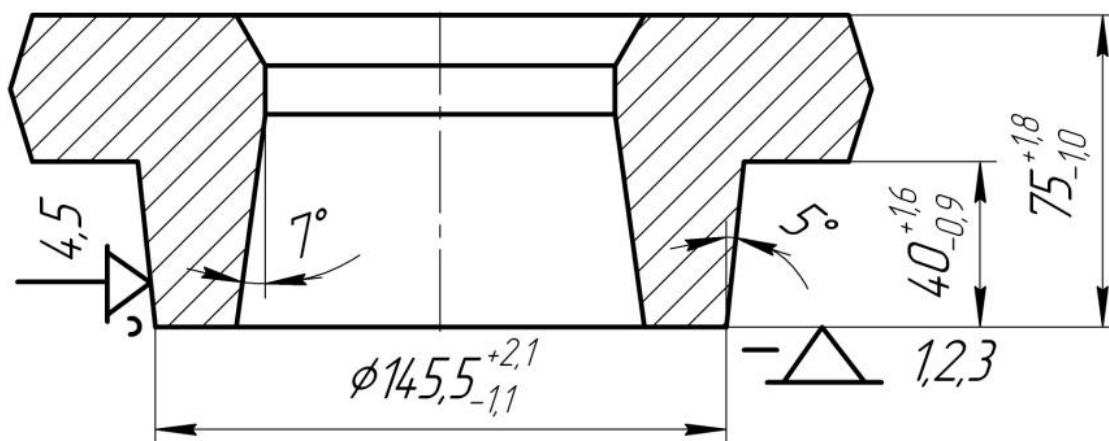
Ескіз заготовки на завантажувальній позиції I
